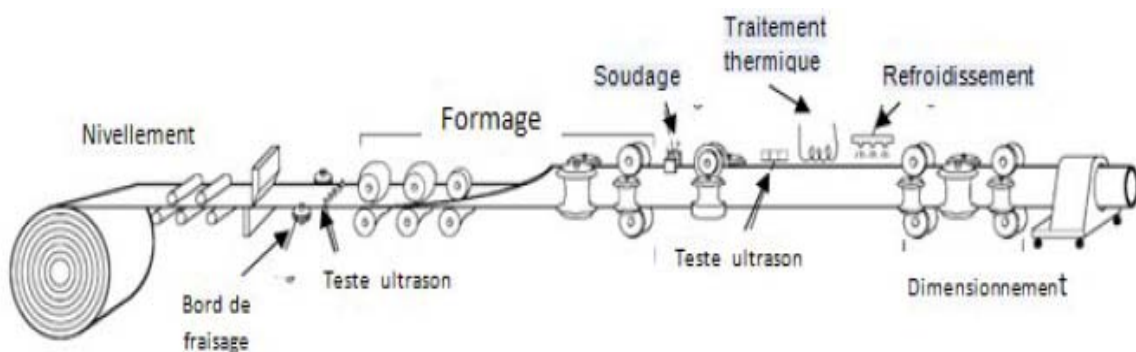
Technique de fabrication des tubes soudés en spirale.
